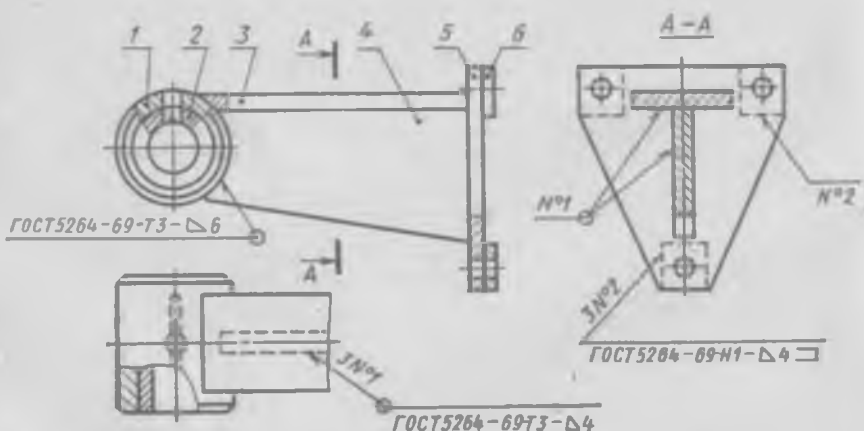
Сварная конструкция подшипника на кронштейне
